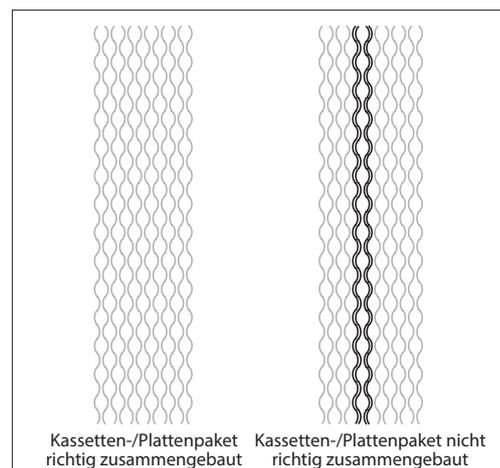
Richtig/Falsch zusammengebautes Plattenpaket
